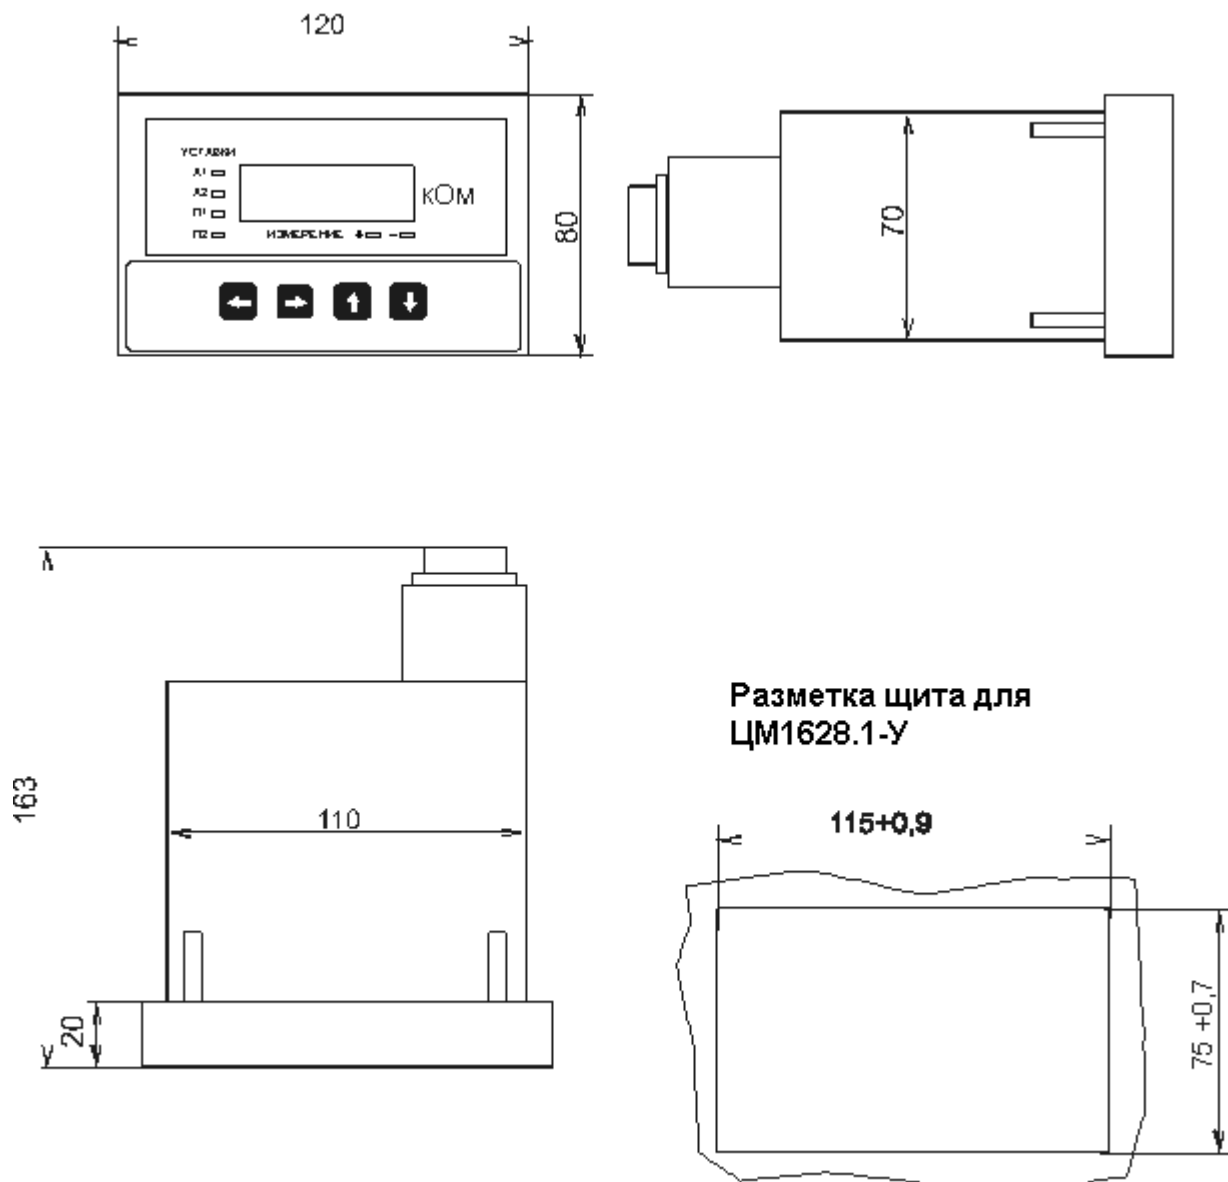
Внешний вид и габаритные размеры блока ЦМ1628/1
